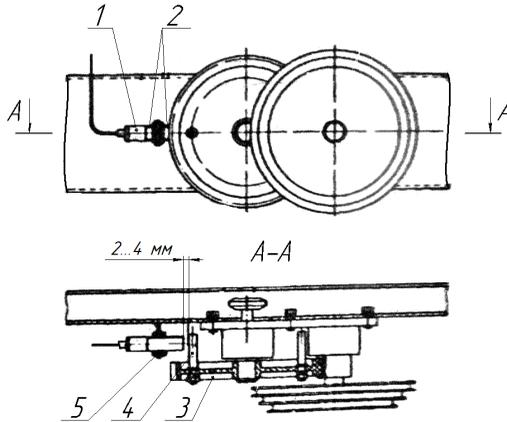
Схема регулировки датчика на обматывающем аппарате:
